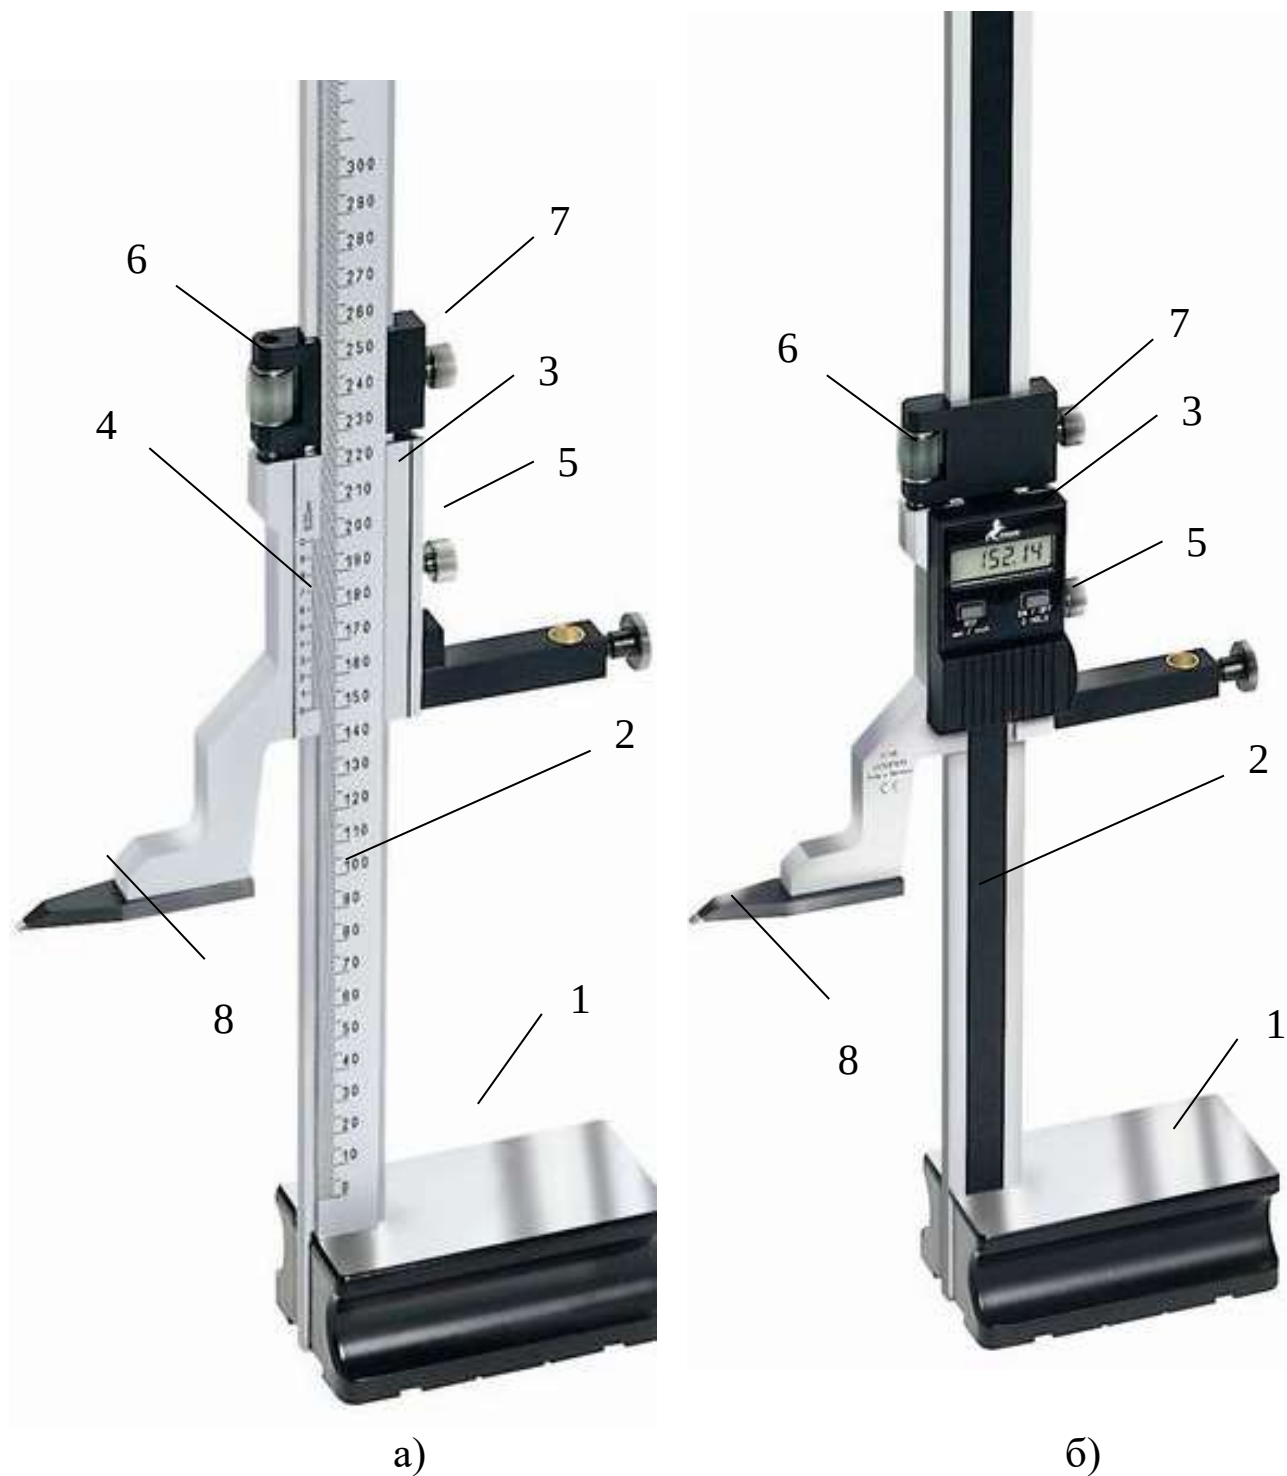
Штангенрейсмус: а) з мікрометричною подачею;
